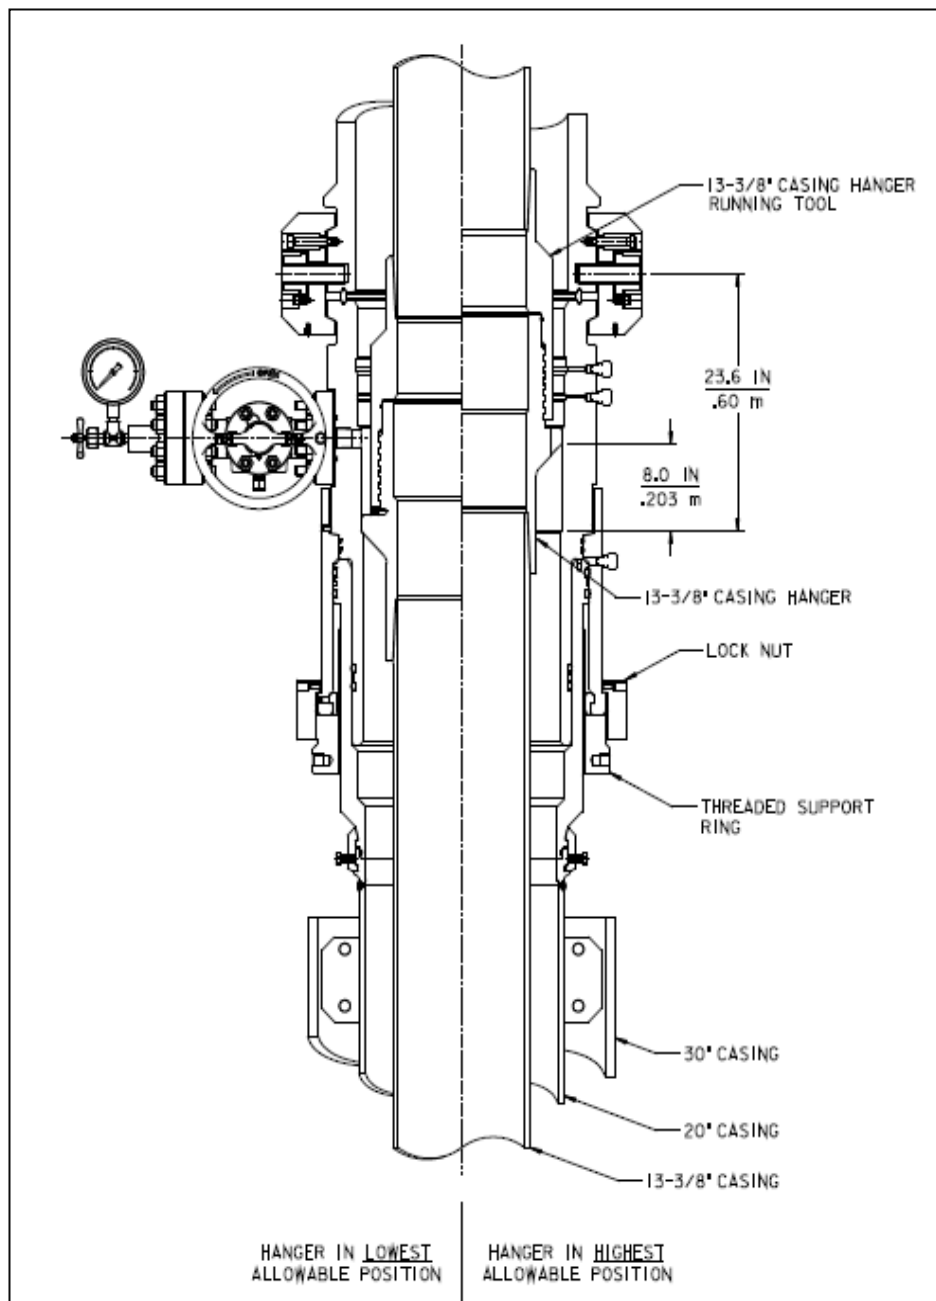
13 3/8" Casing Hanger dans l'ajustable Casing Head.
